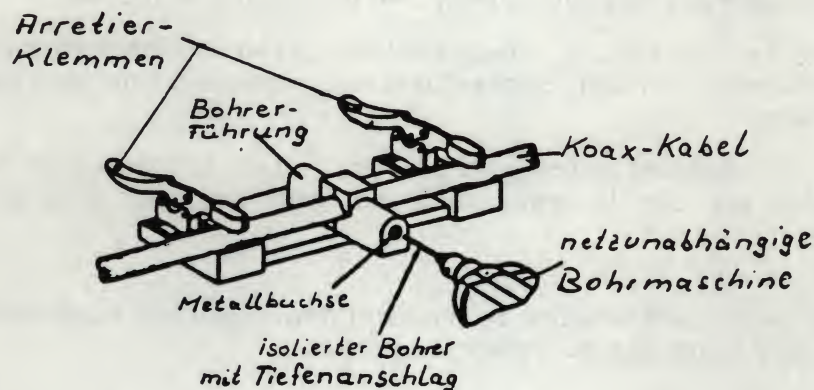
Bohrvorrichtung mit Bohrerfuehrung
